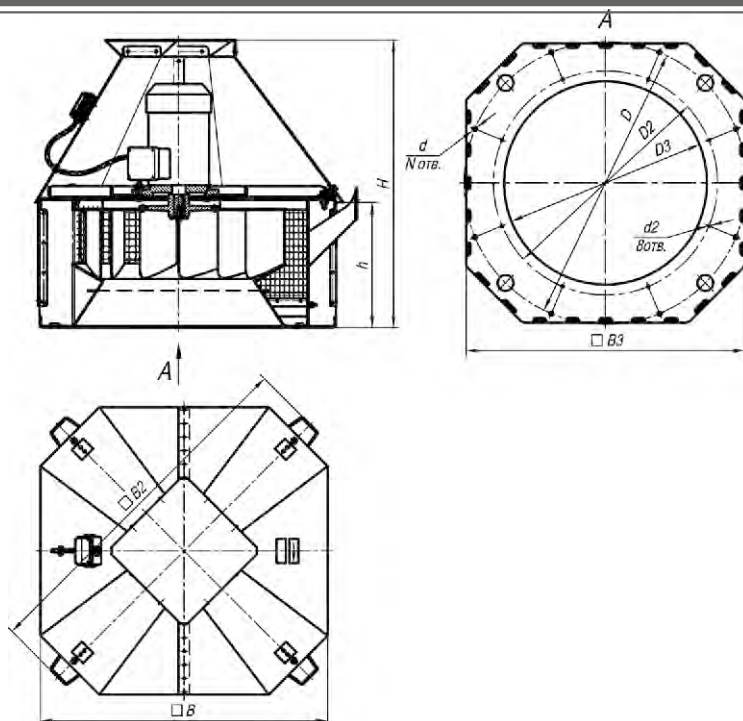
Габаритные и присоединительные размеры ВКРм №3,15-№10 исп-1.
